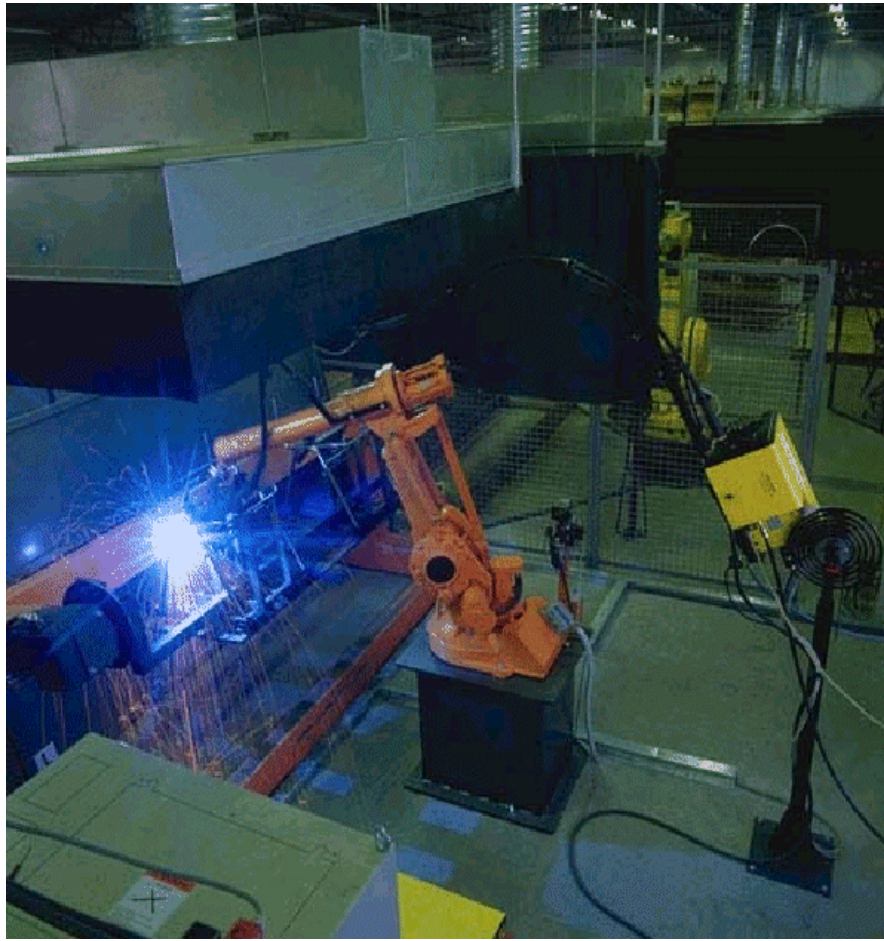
Aplicación de robots en tipos de soldadura (de puntos, soldadura de arco), pintura y otros
